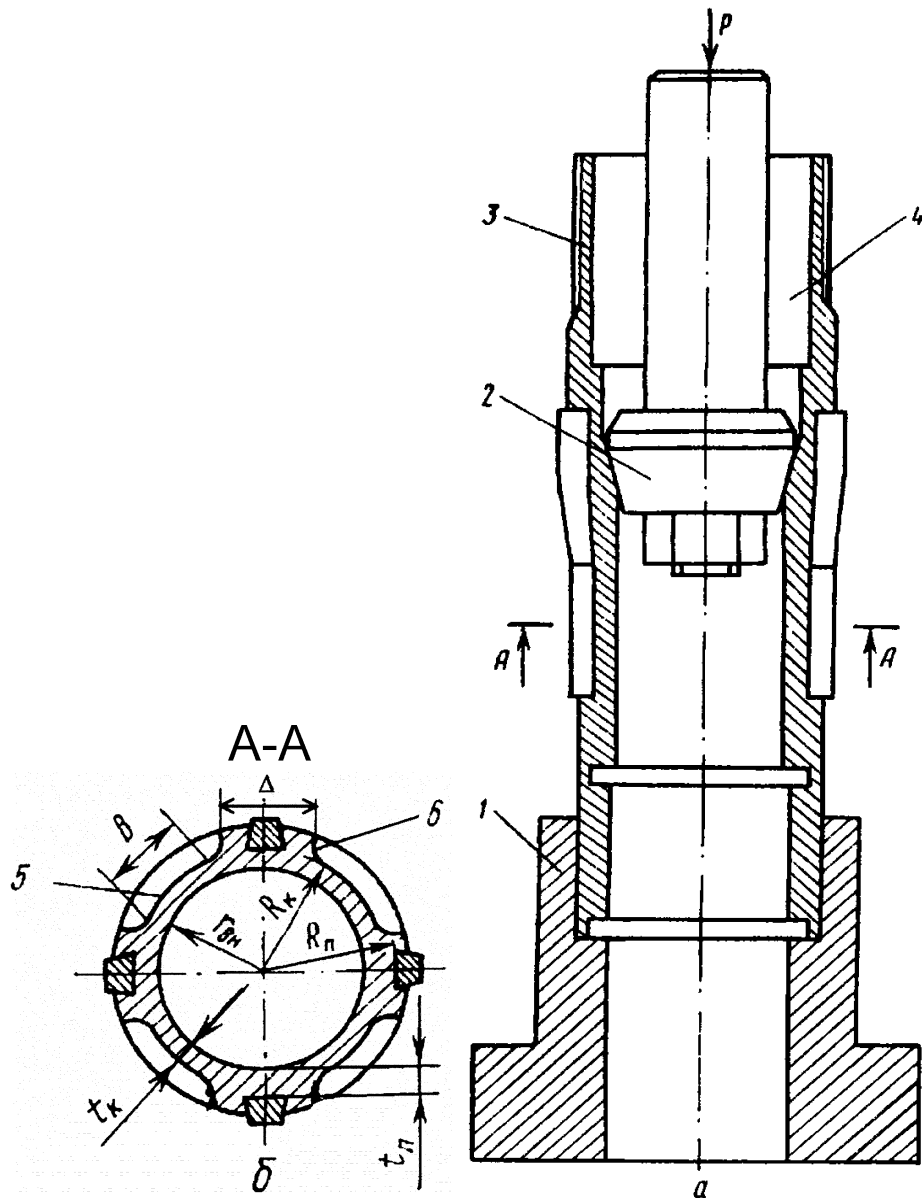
Схема роздачі (б) і поперечний переріз розширювача (а): 1 – опора; 2 – деформуючий елемент; 3 – розширювач; 4 – виточки; 5 – канавки в корпусі; 6 – бічні поверхні канавок
